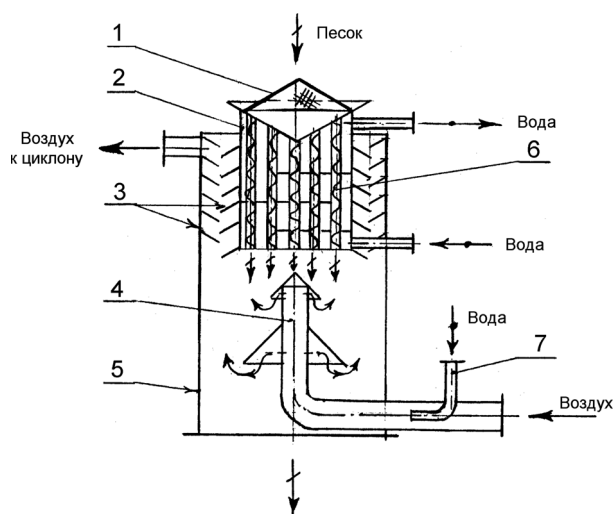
Установка охлаждения сыпучего формовочного материала комбинированным способом: 1 - сетчатый колпак; 2 - водоохлаждаемый корпус; 3 - отражающие пыль кольца; 4 - воздухоподводящий патрубок; 5 - наружный корпус
